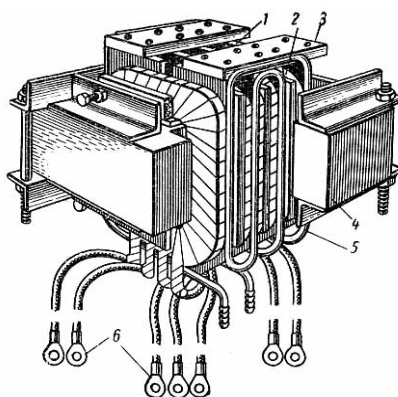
Сварочный трансформатор контактной машины
